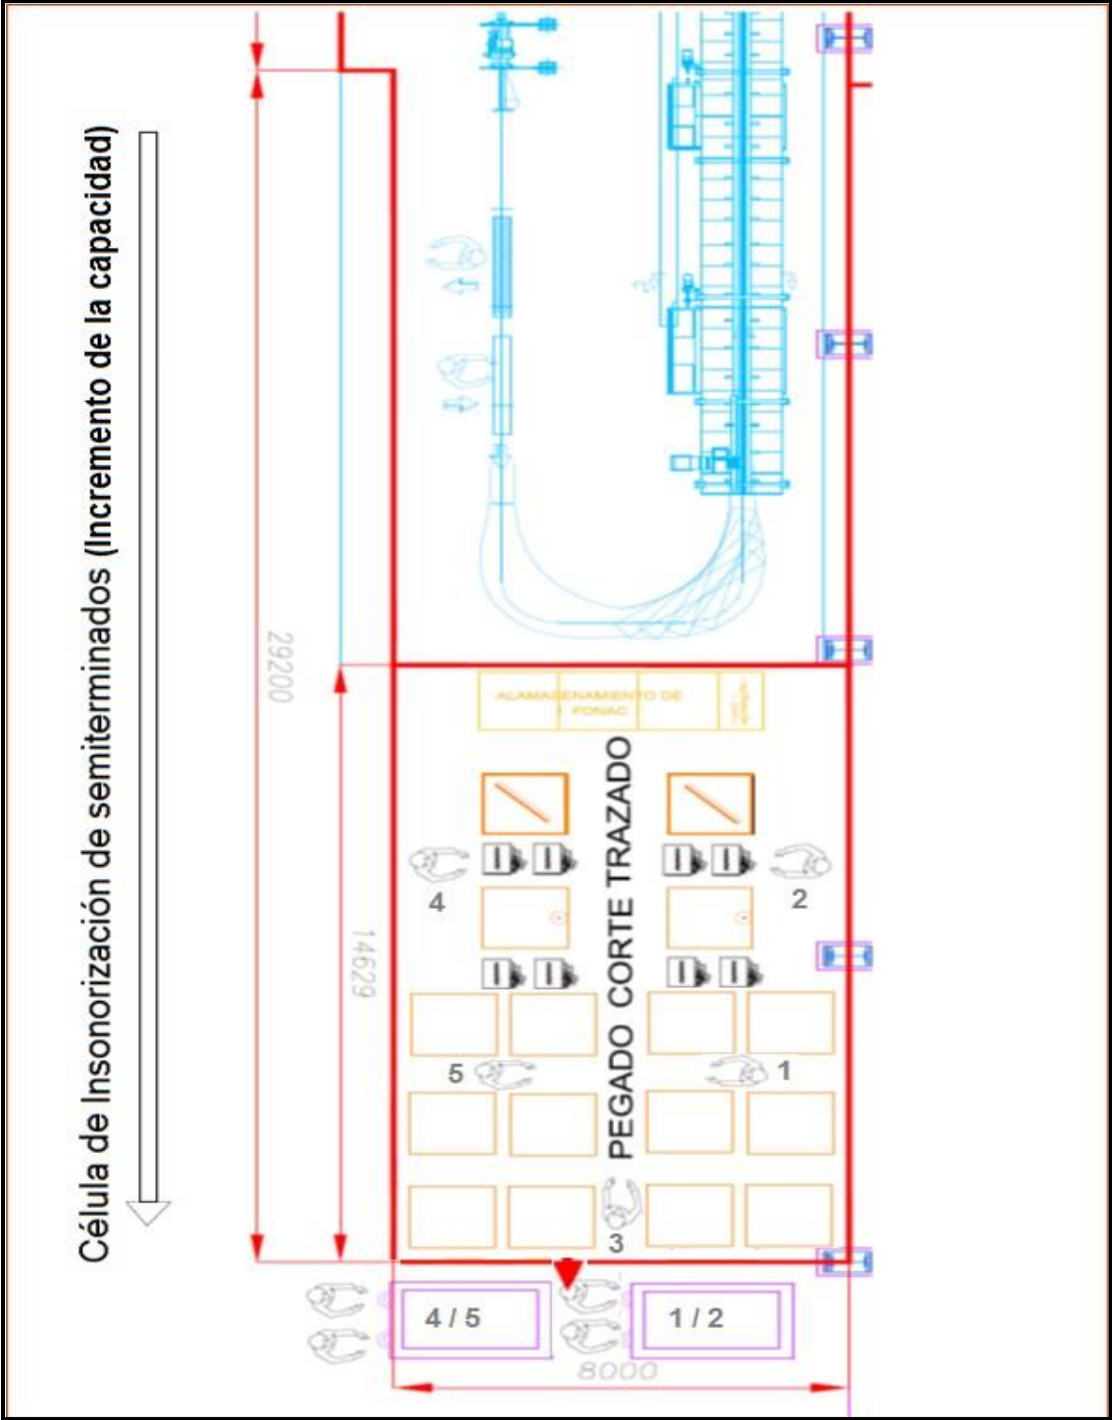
Distribución en planta luego de incrementar la capacidad de la restricción
